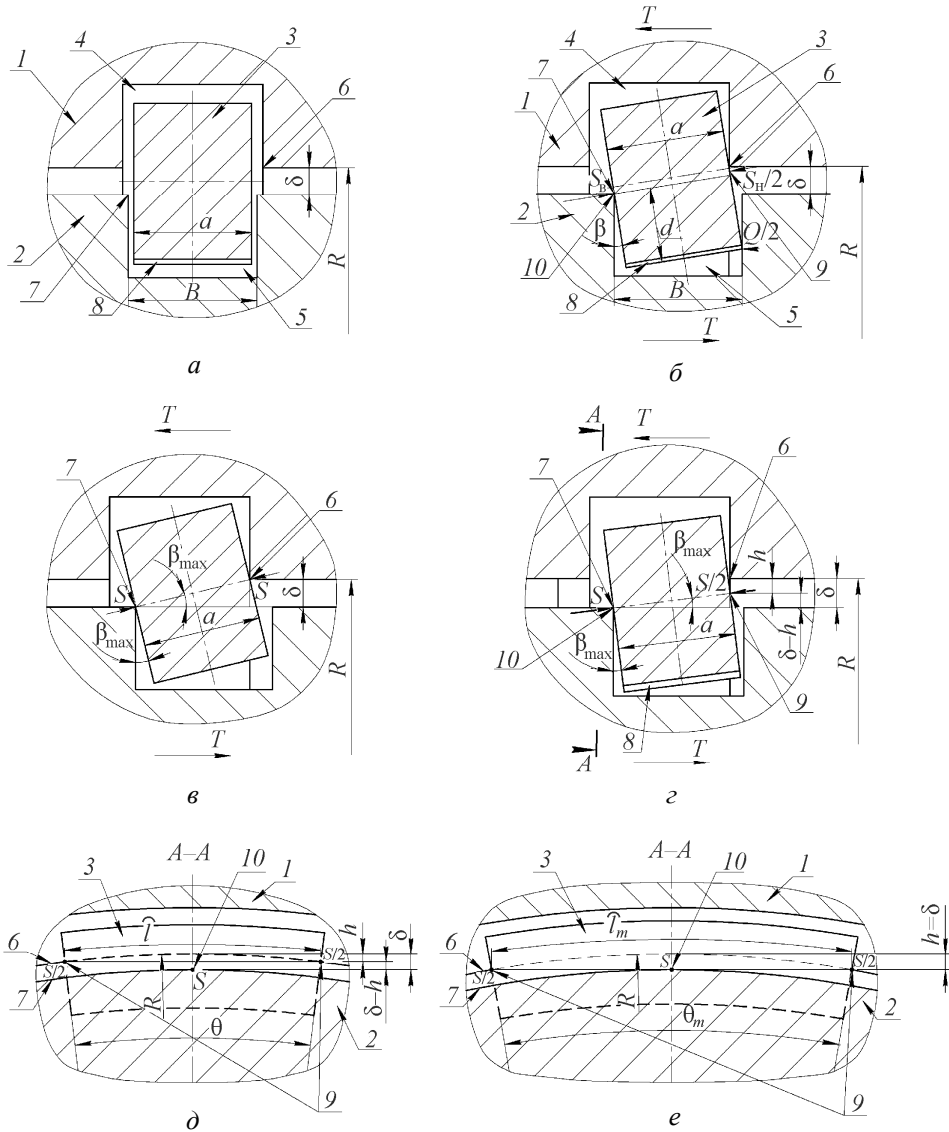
Схема работы шпоночного соединения: 1 – наружный шпангоут; 2 – внутренний шпангоут; 3 – шпонка; 4 – шпоночный паз наружного шпангоута; 5 – шпоночный паз внутреннего шпангоута; 6 – ребро шпоночного пазы наружного шпангоута; 7 – ребро шпоночного пазы внутреннего шпангоута; 8 – цилиндрическая поверхность шпонки; 9 – точка приложения силы от ребра шпоночного пазы наружного шпангоута; 10 – точка приложения силы от ребра шпоночного пазы внутреннего шпангоута
